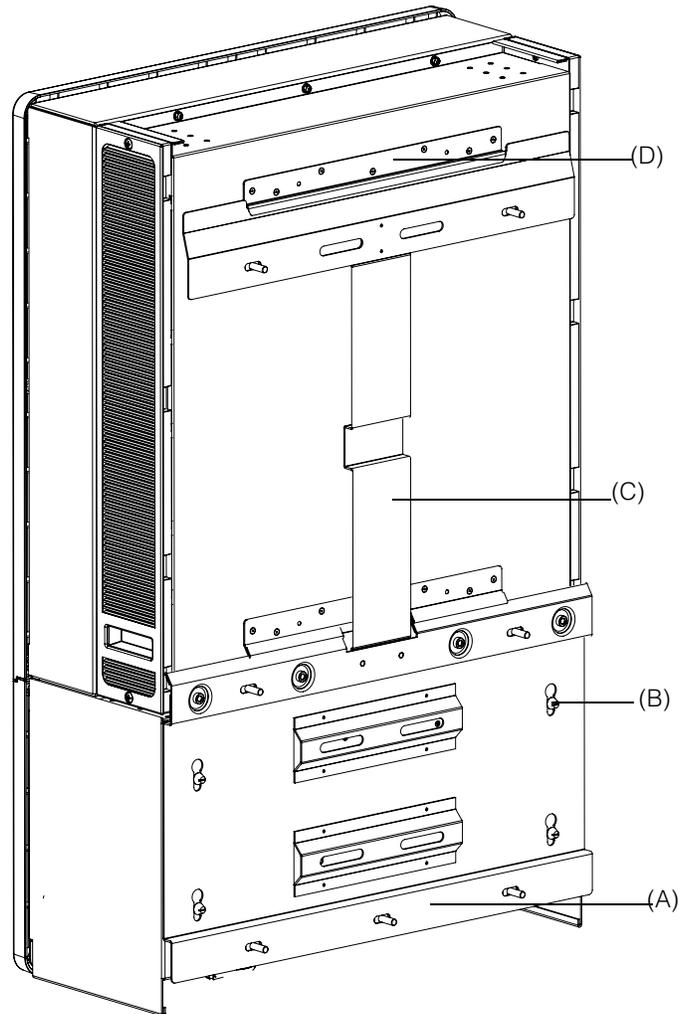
Vue arrière de l'onduleur équipé de son support de montage
